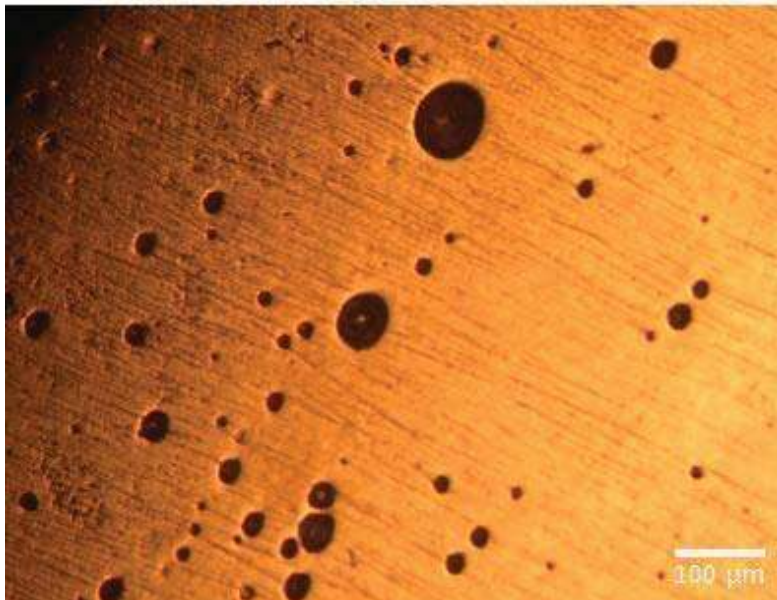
Porosidad presente en el cordón de soldadura
